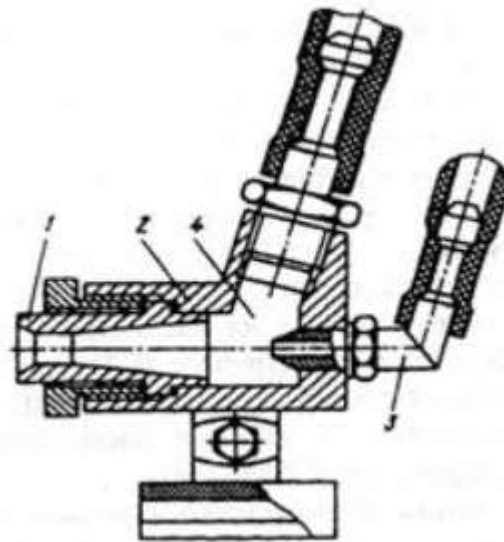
Робоче сопло: 1 - змінна насадка, 2 – корпус, 3 – форсунка подачі повітря
